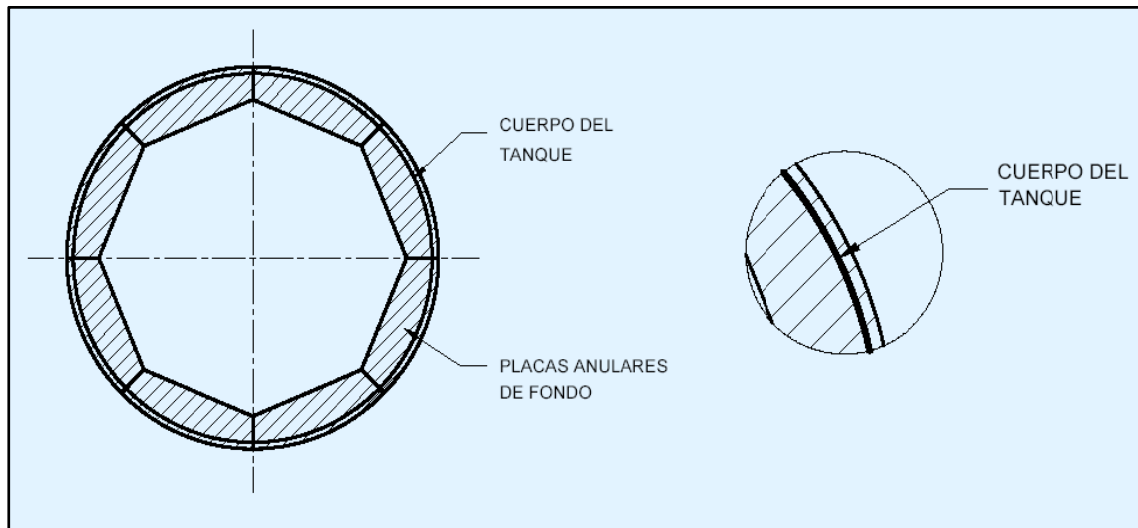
Placa anular formada por segmentos soldados a tope
